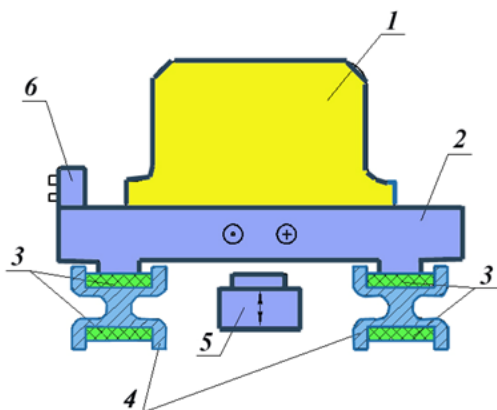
Схема пристрою транспортування палет на конвеєрі: 1- виріб; 2 - палета; 3 - нескінченні стрічки конвеєра; 4 - несучі профілі з порожниною повернення стрічки; 5 - висувний упор для зупинки супутника; 6 - носій коду
